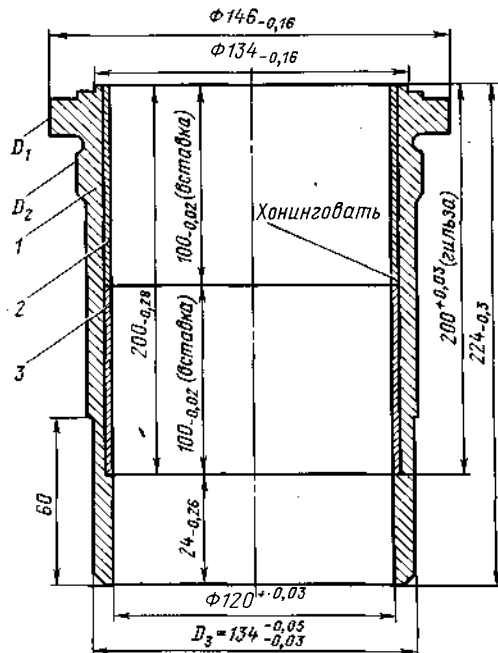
Геометрические размеры гильзы цилиндров КамАЗ-740, восстановленные под размеры по рабочему чертежу:
